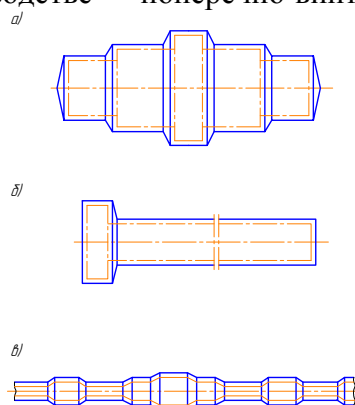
Заготовки для валов полученные различными способами: а) - штамповка в подкладных штампах; б) – штамповка на горизонтально-ковочной машине; в) – поперечно-винтовая прокатка.
